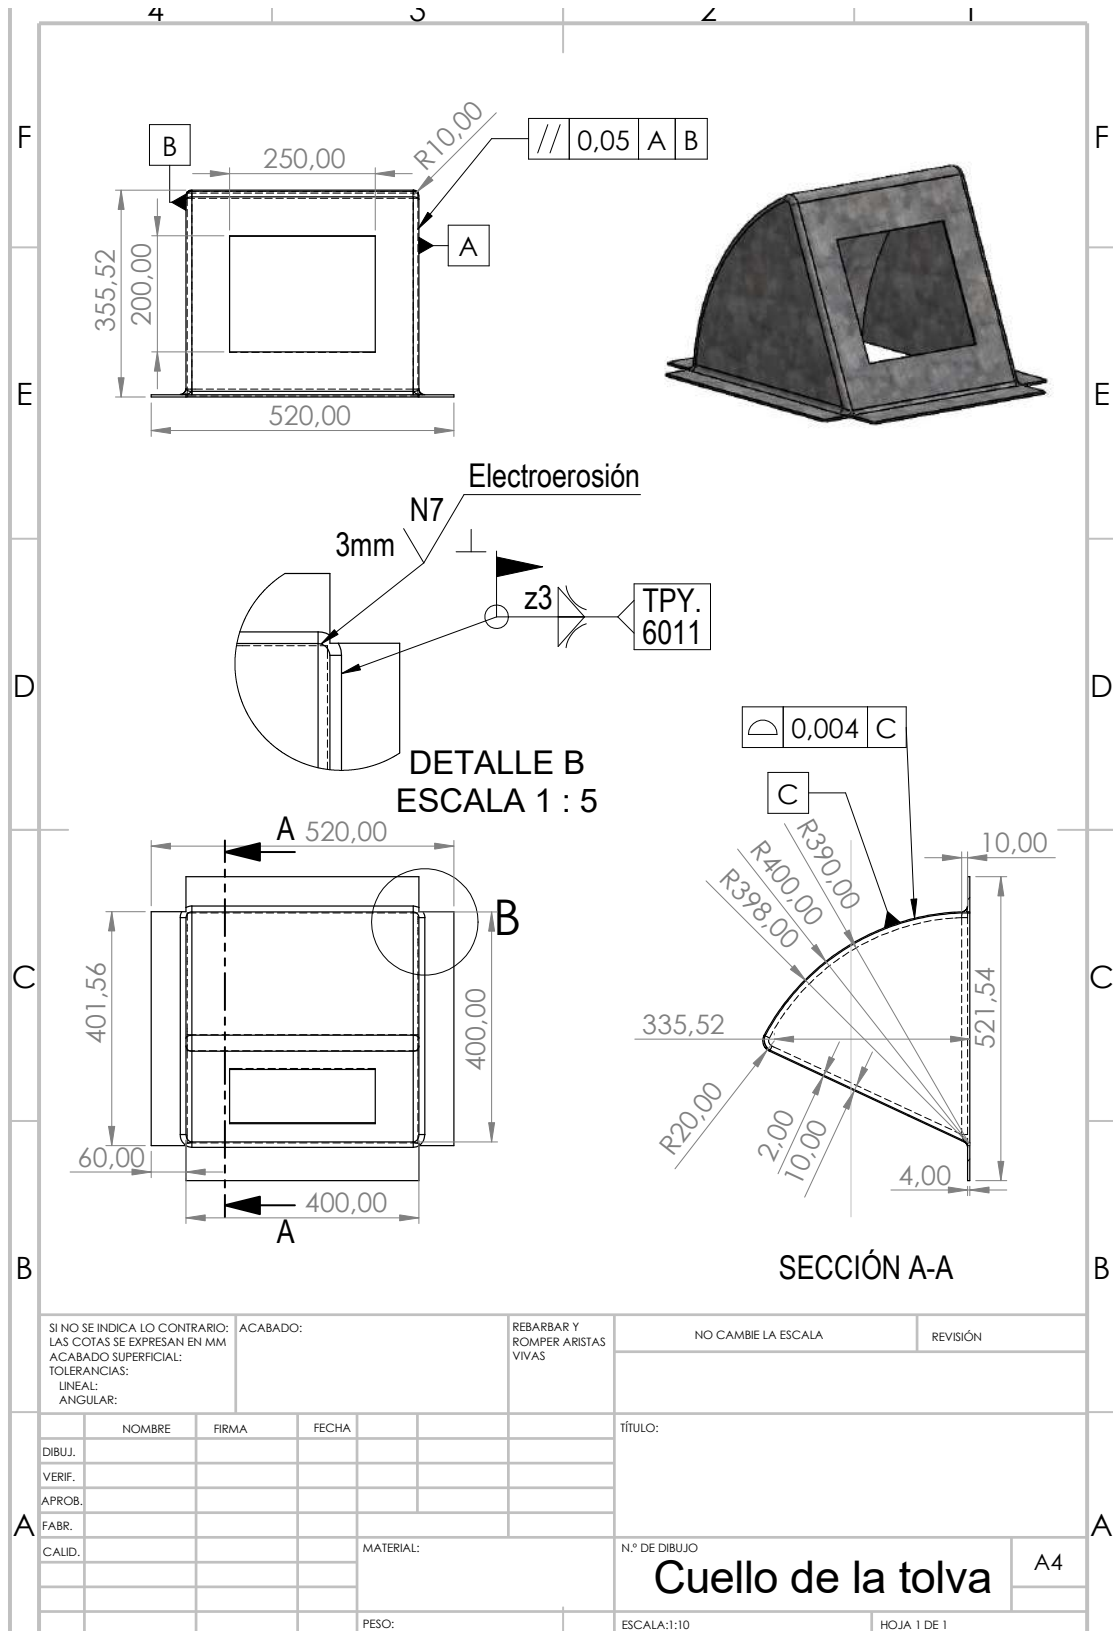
Plano del cuello de la tolva. Fuente: Los autores.
